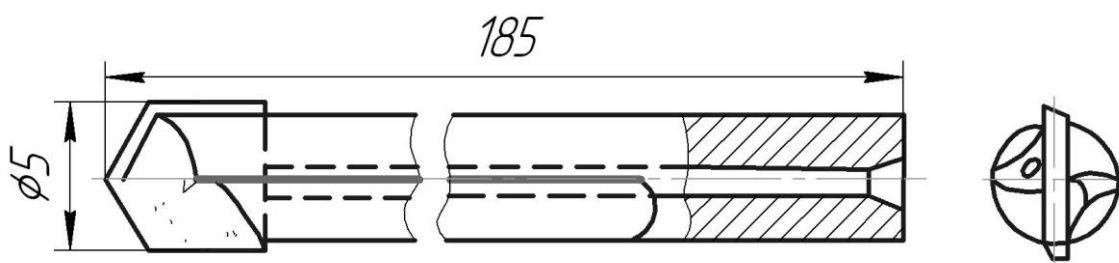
Сверло с напайкой из твердого сплава для вибросверления глубоких отверстий малого диаметра
